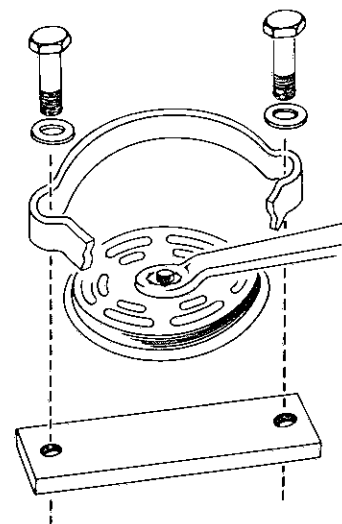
Spezialwerkzeuge für die Einspannung der Ventile in den Schraubstock
